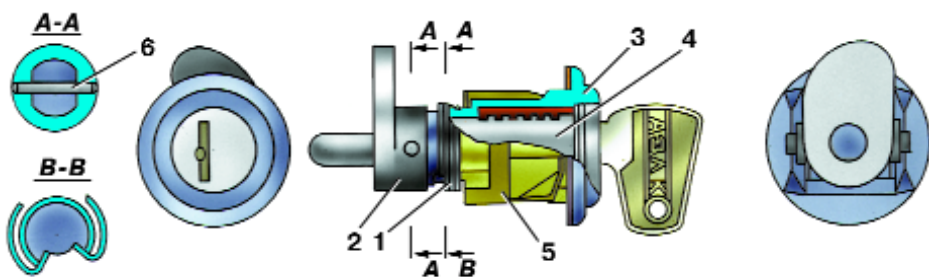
Выключатель замка двери задка: 1 – возвратная пружина; 2 – кулачок; 3 – корпус выключателя; 4 – цилиндр; 5 – пружинный держатель; 6 – штифт кулачка
